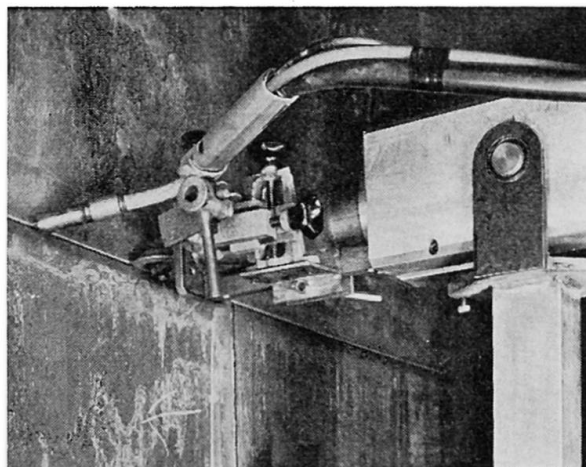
Apparatur eingestellt für vollautomatisches Schweißen einer Horizontalnaht (Detailaufnahme).
